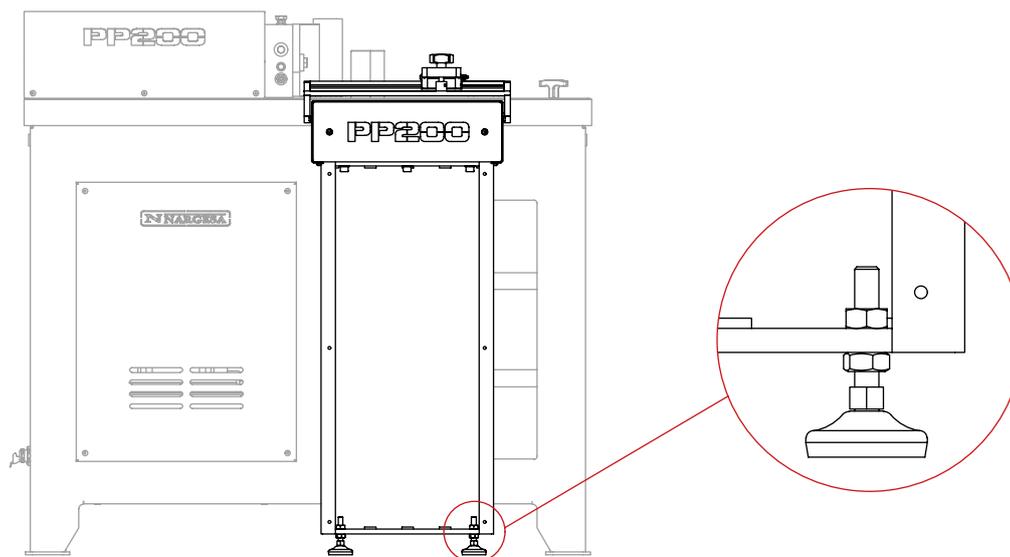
Nivellement final de la butée et vue détaillée des pieds réglables
